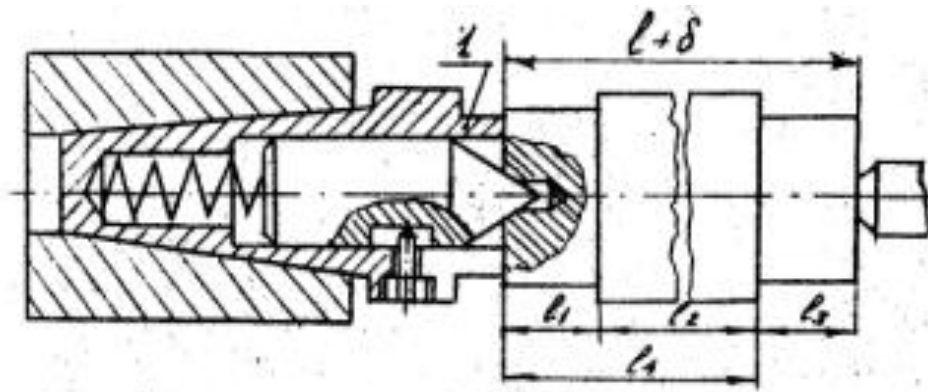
Схема установки деталі "вал" на плаваючий передній центр
